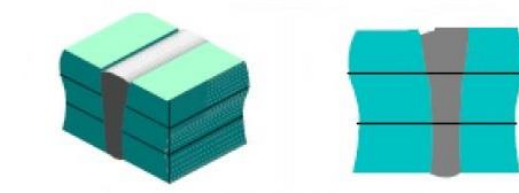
Schweißnahtfehler „Einbrandkerben“ [6]
